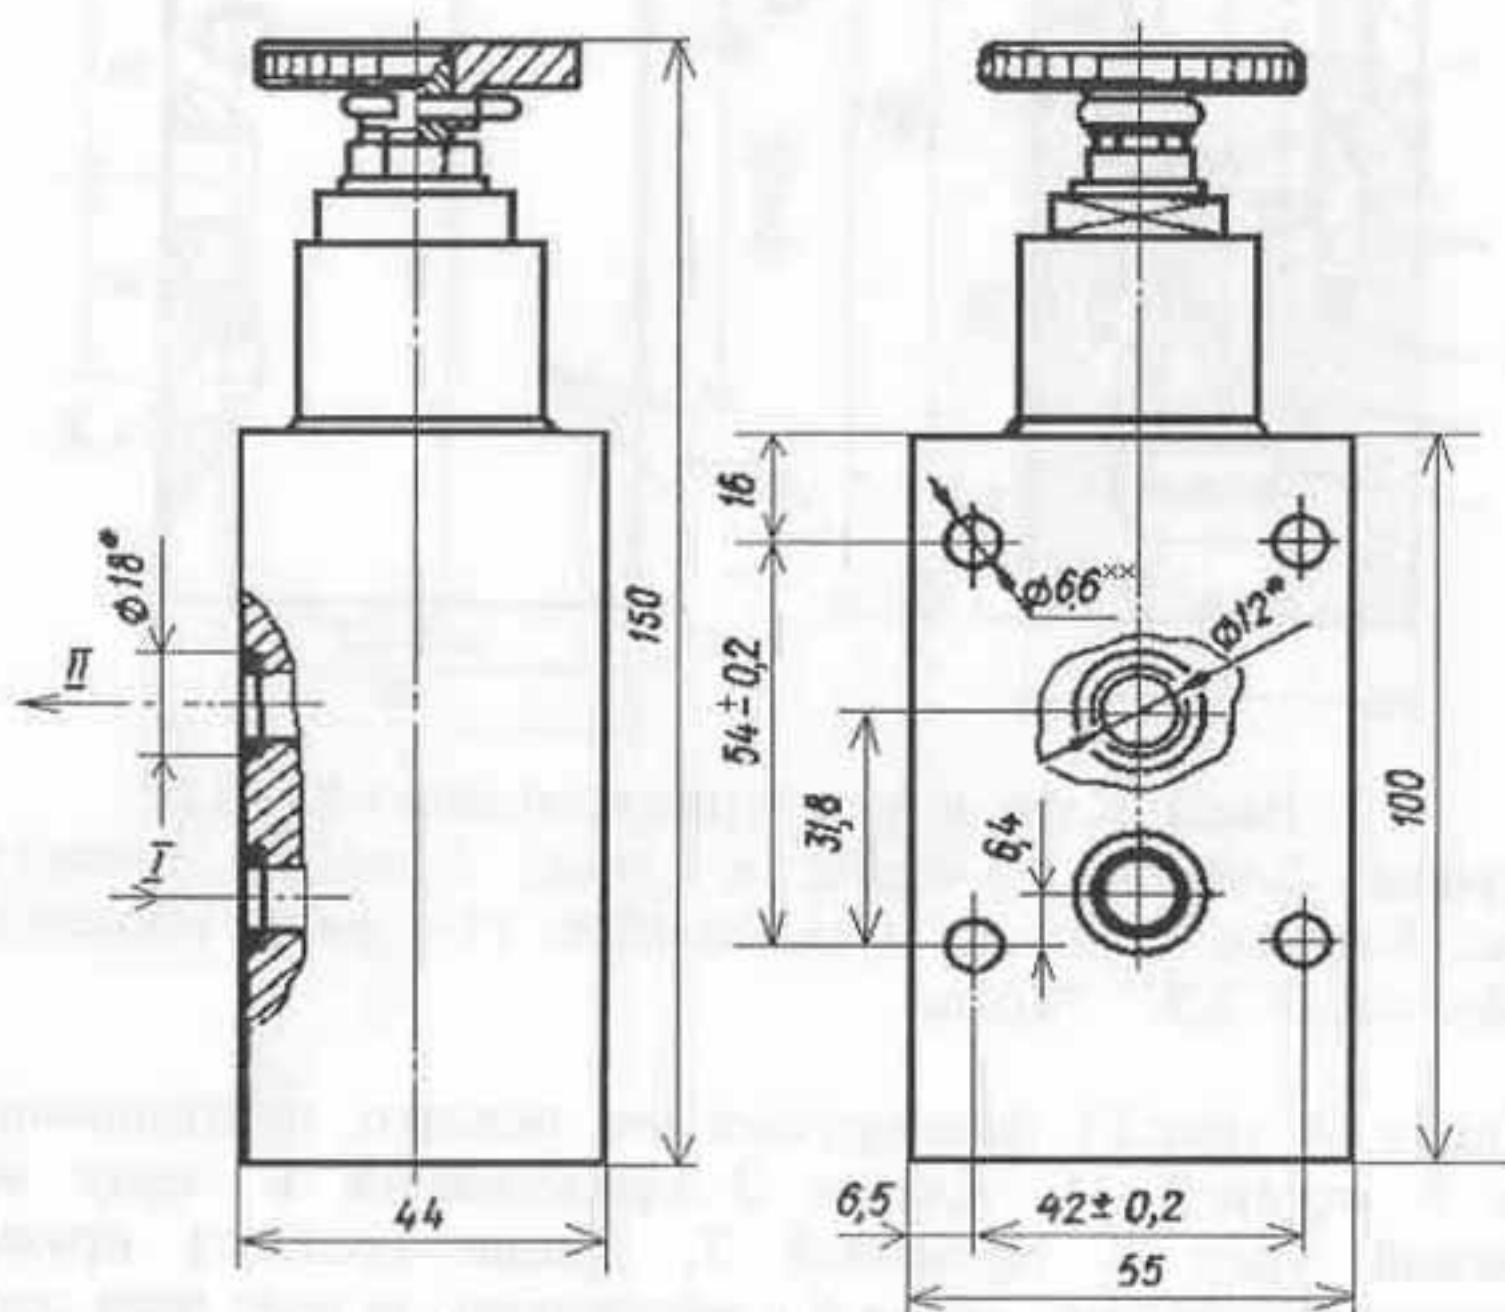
Клапан предохранительный СКПС12/: I — подвод; II—отвод;
